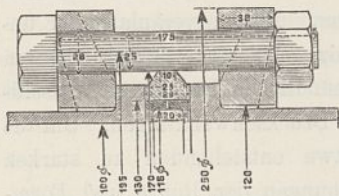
Flanschdichtung der 100 mm im Lichten weiten Druckwasserleitung.
